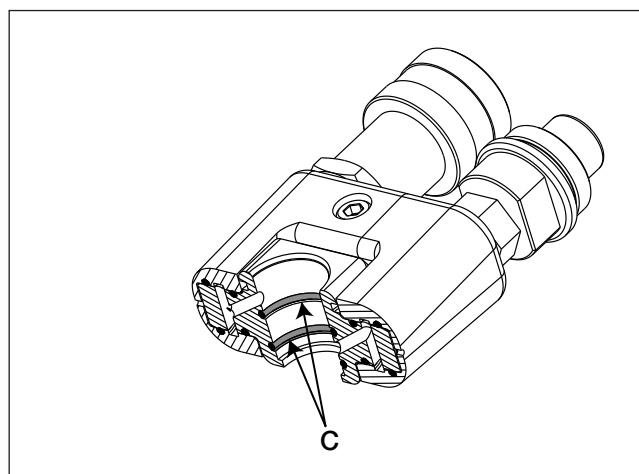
Установка уплотнительного кольца - Блок поворотного коллектора
